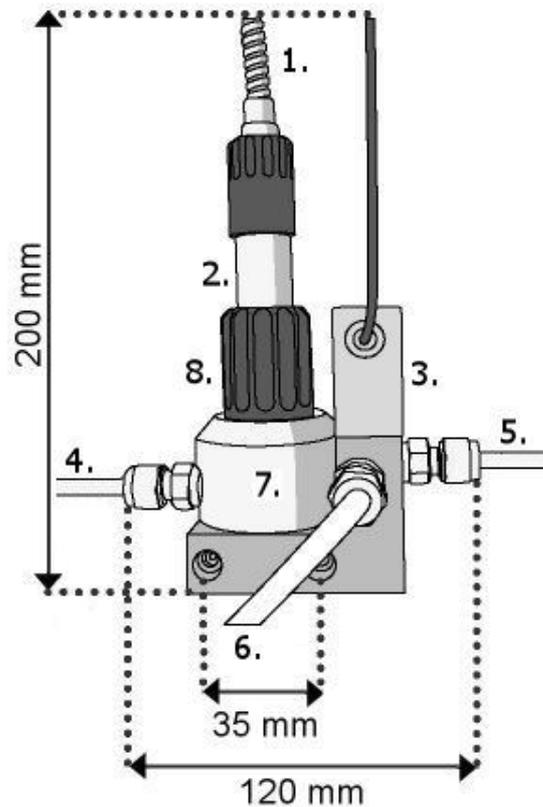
Dimensiones y componentes de la cámara de flujo
